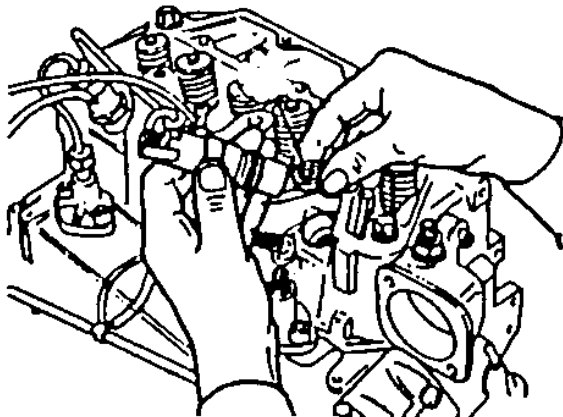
Проверка и регулировка форсунок на давление впрыска и качество распыла топлива.
